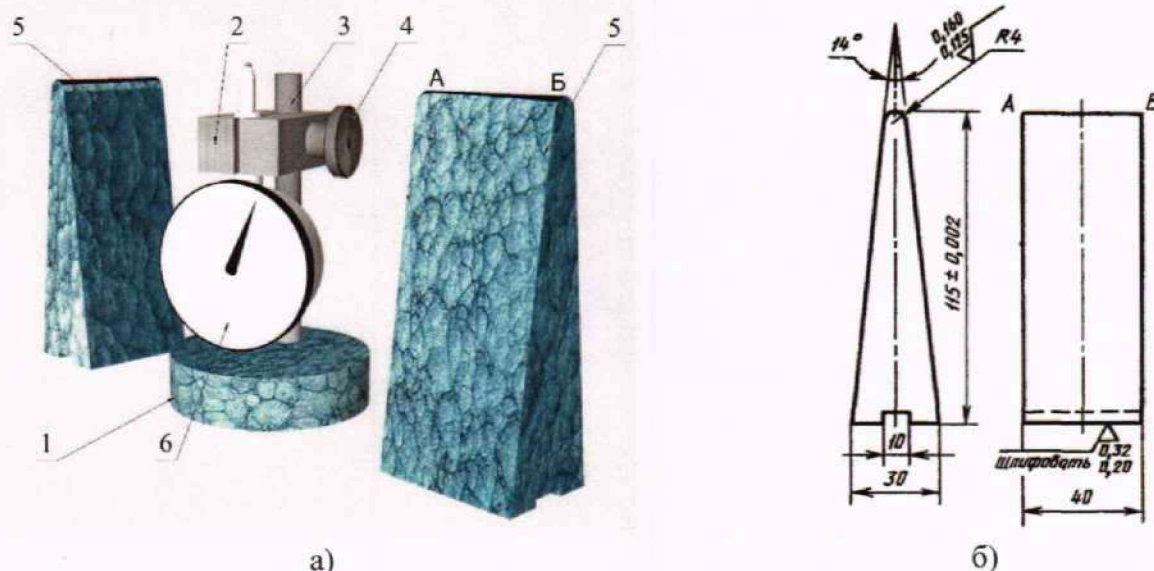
Приспособление для измерения отклонения от плоскостности методом сличения с поверочными линейками: а) – общий вид приспособления; б) – опорная призма
